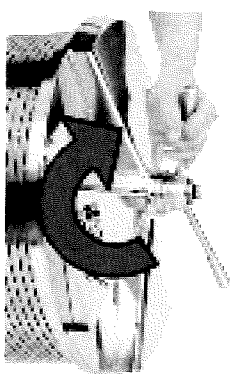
Aufschrauben der Gewindemutter auf die Gewindespindel der Einlassachse
